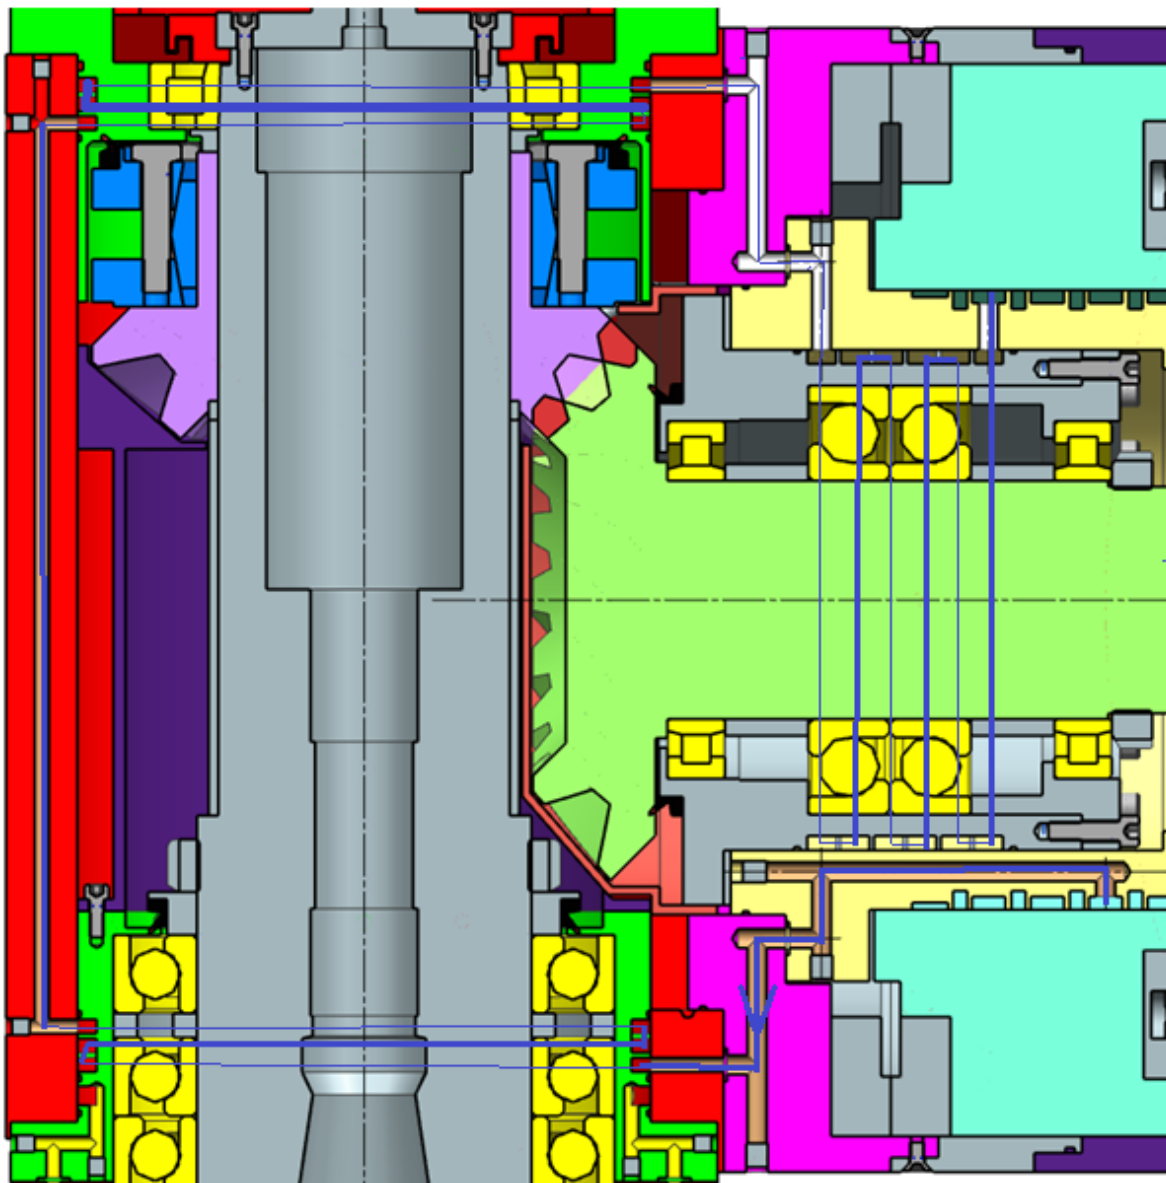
Zakrytování ozubení; Těsnění a odfuk
